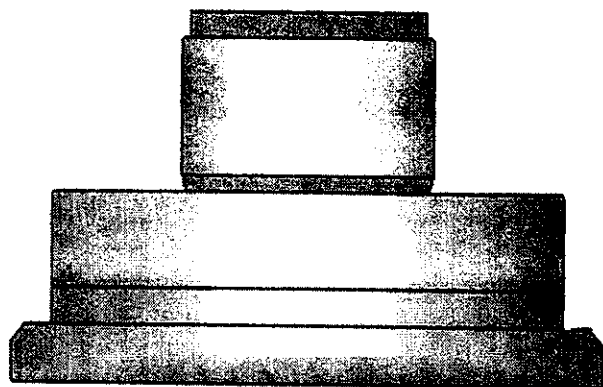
Крышка ковша печи из металлического кожуха с размещенными внутри трубами водяного охлаждения
